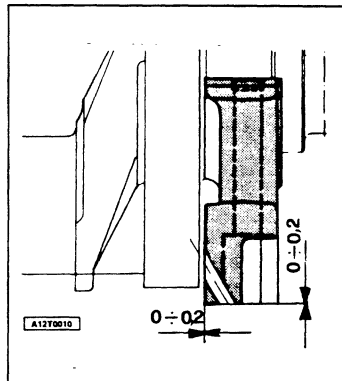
Montaje de las guarniciones de los soportes de banco.
